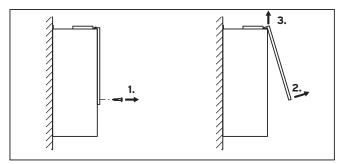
Desmontaje de la placa frontal (cámara de depresión)
